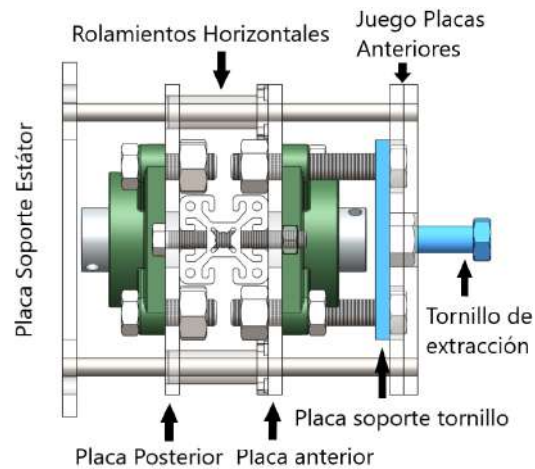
Ensamblaje de la placa base y el tornillo de extracción del estátor.
